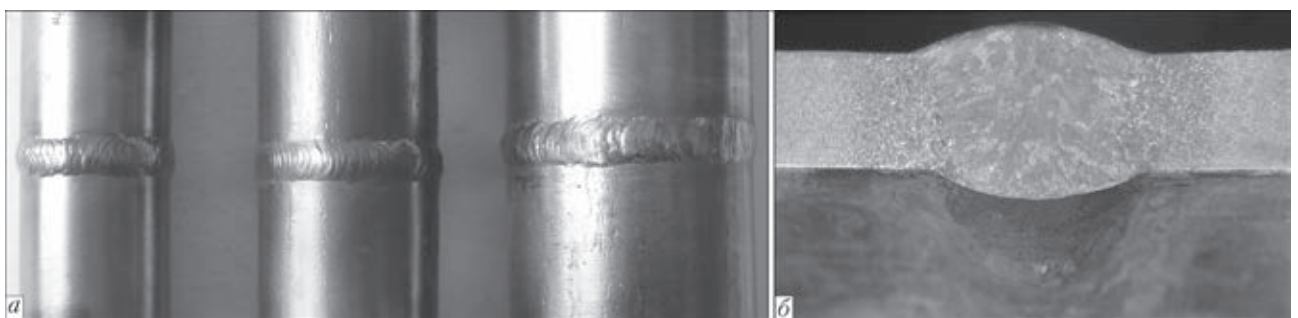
Стыковые соединения труб поверхности нагрева: а — внешний вид соединений; б — поперечное сечение соединения
